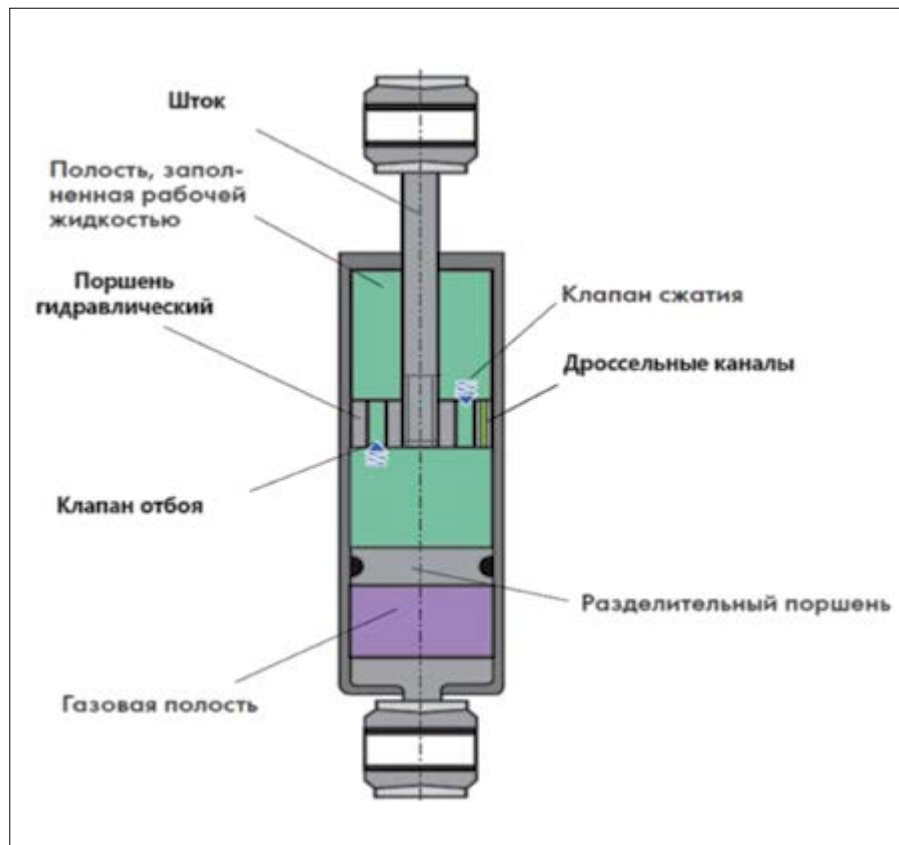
Типовой однотрубный гидропневматический амортизатор
